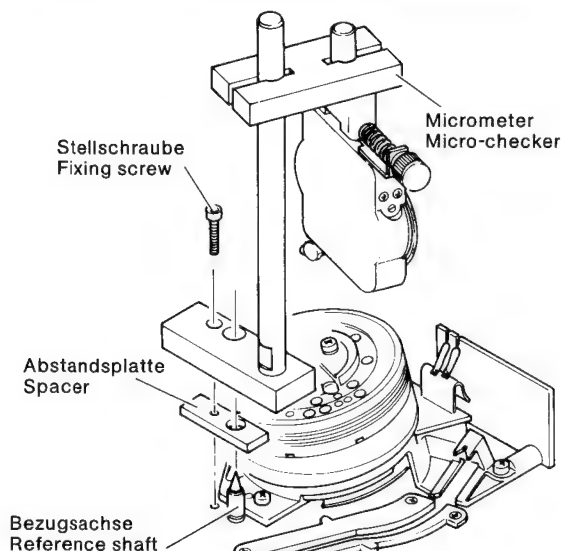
Anbringung der Mikrolehre / Micro-checker mounting
